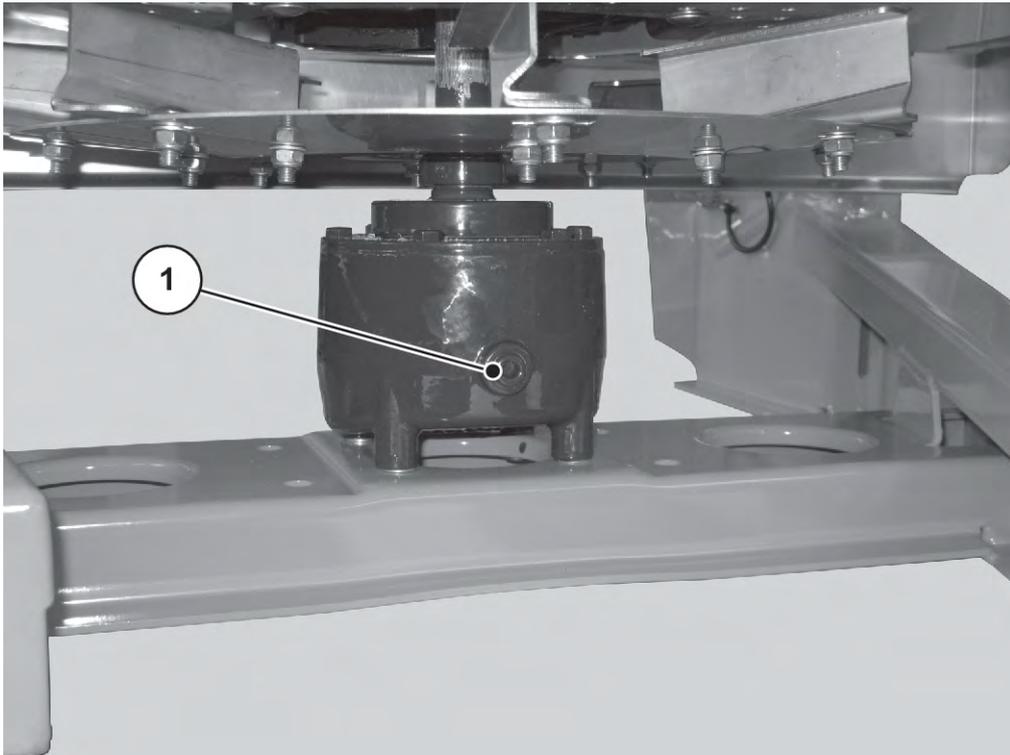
Kontrollschraube für Getriebe-Ölstand
